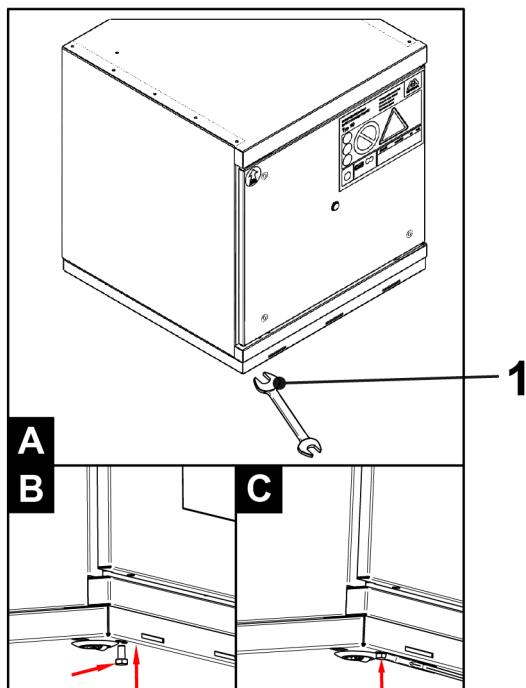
Montaggio e utilizzo delle viti di serraggio
